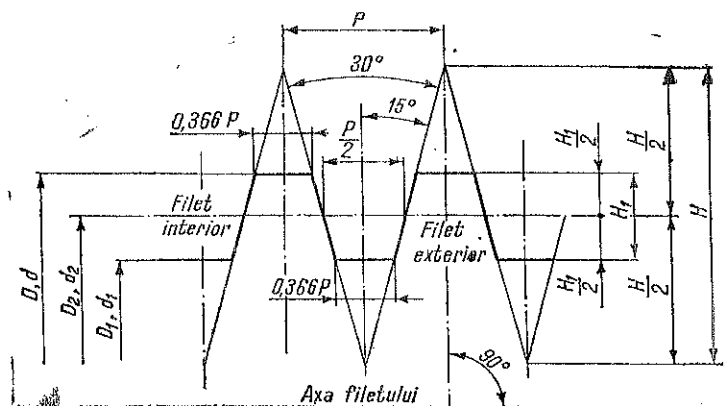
Profilul de bază al filetelor trapezoidale ISO.
